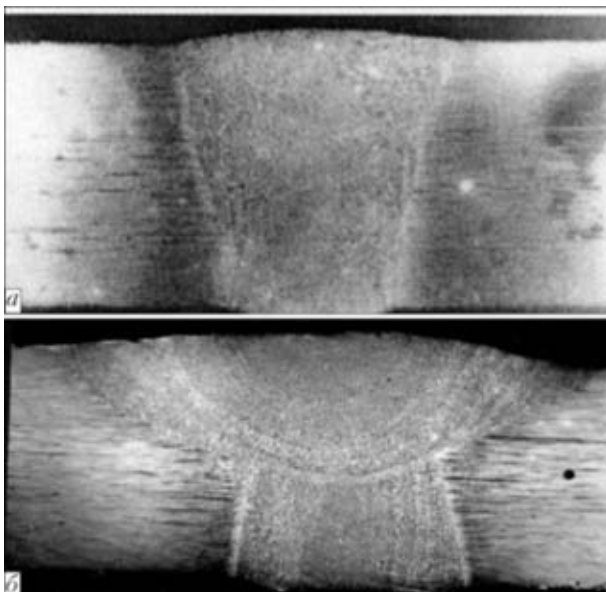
Макрошлифы одно- (*а*) и двухслойного (*б*) швов
